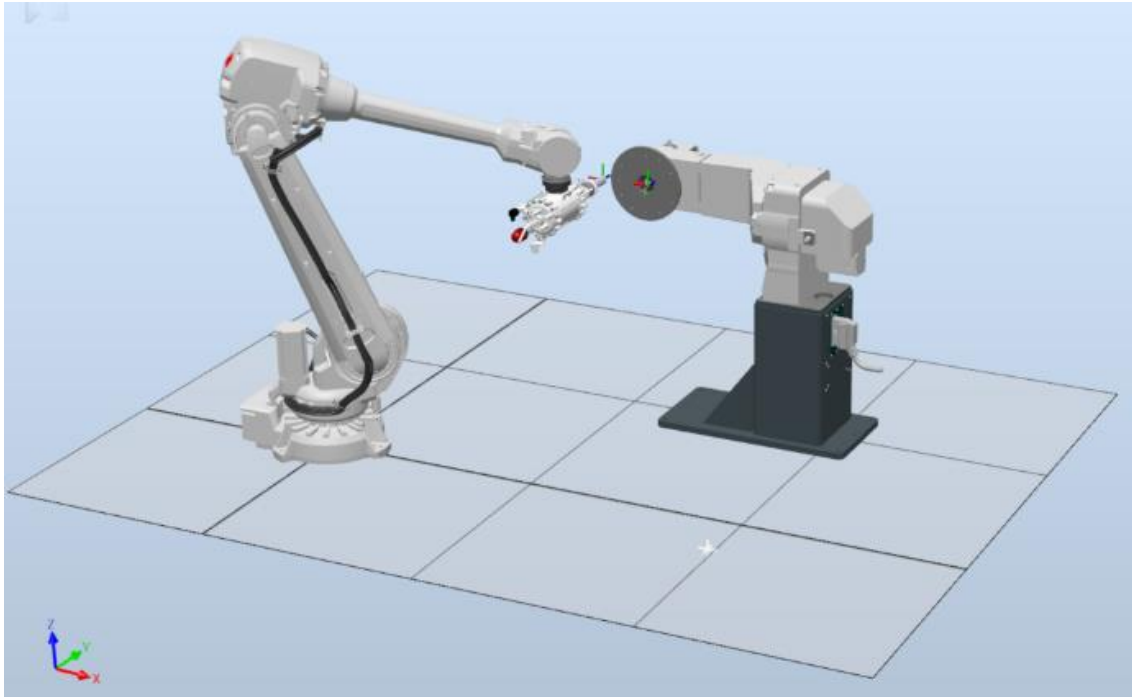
Robotická ruka ABB IRB 4600 [16]
